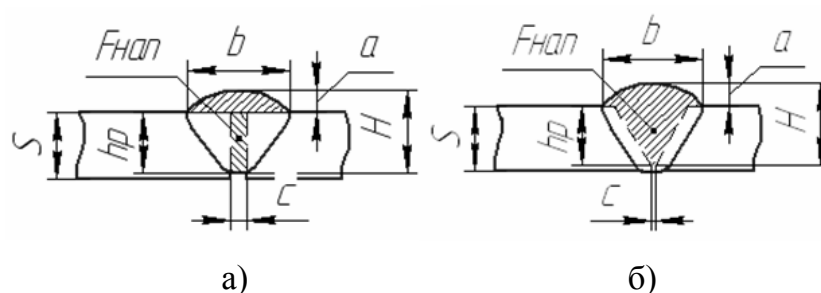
Стыковое соединение без разделки кромок для сварки под флюсом по ГОСТ 8713–79 (а); с разделкой кромок для сварки в среде защитных газов по ГОСТ 14771–76 (б)
